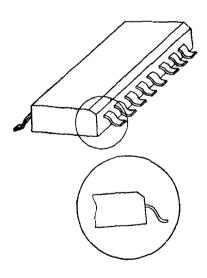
Корпус типа Ф → Рис. 6.12. Безвыводной корпус типа Н
